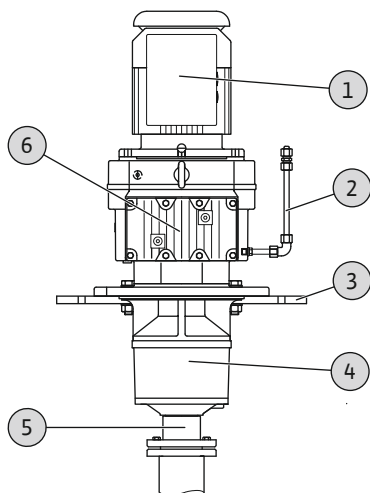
Piedziņas bloka konstrukcijas detaļas
